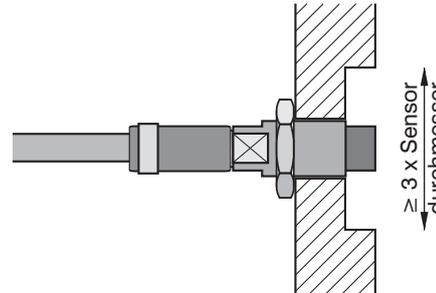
Flächenbündige Montage eines ungeschirmten Sensors in einer metallischen Halterung mit Aussparung
